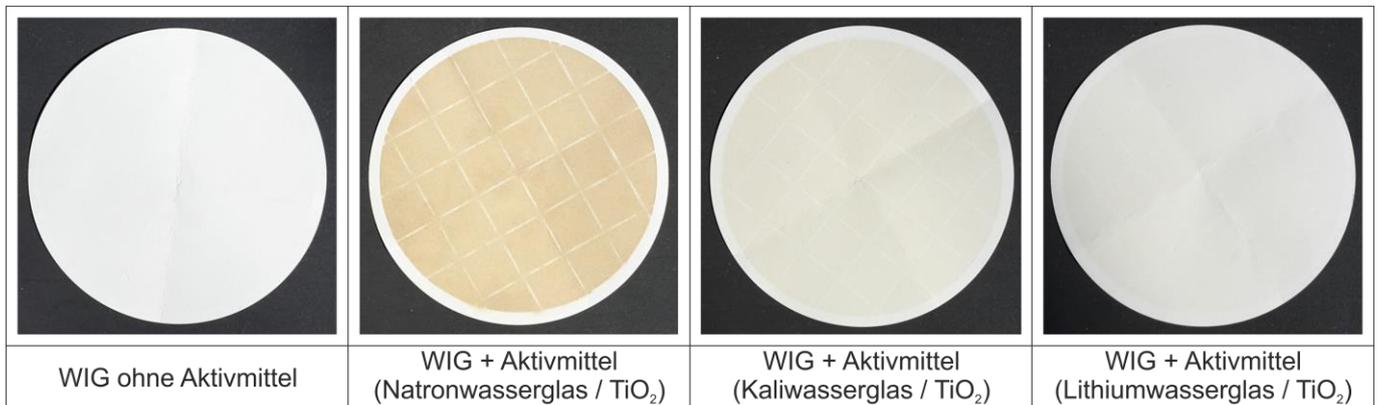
Vergleich der bei Schweißrauchmessungen entnommenen Filter für das WIG-Schweißen ohne und mit Aktivmitteln.
